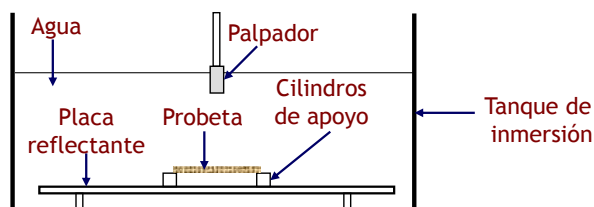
Esquema de colocación de las placas de laminado de material compuesto a inspeccionar por C-Scan
